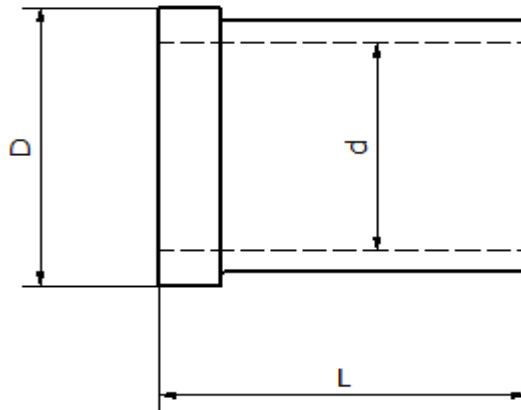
Dimensiones principales del cojinete (Elaboración Propia).
